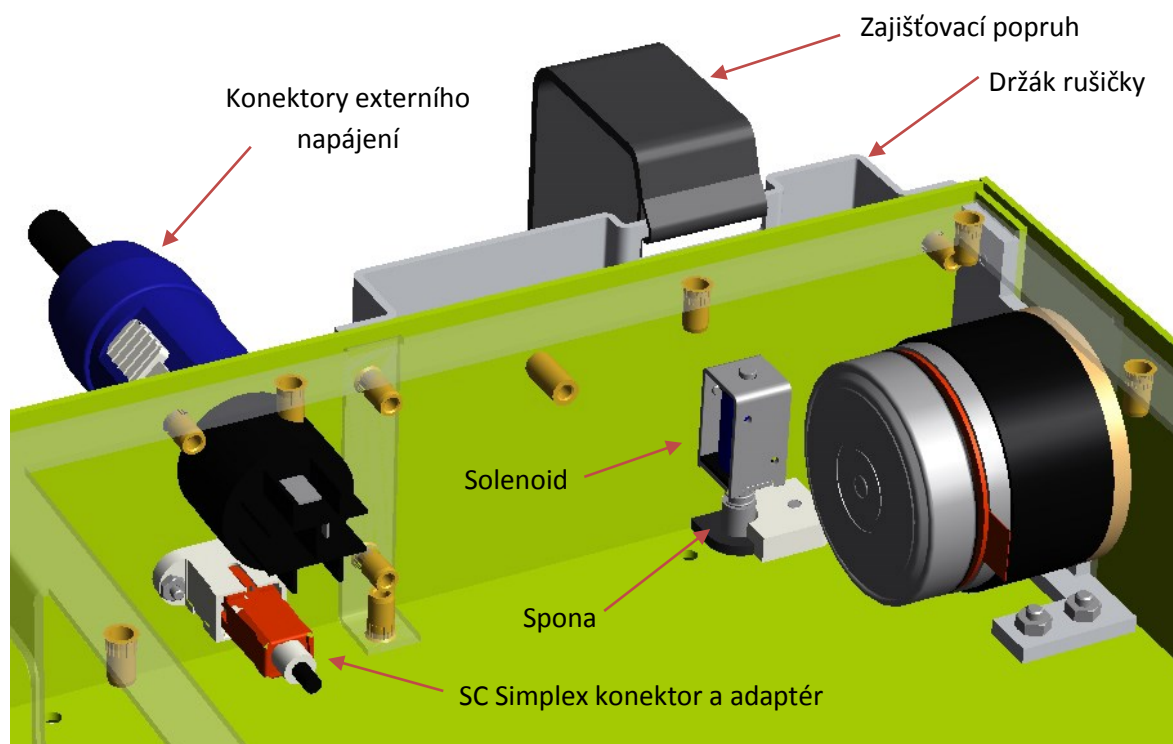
Robot – 3. Stádium – Nosný rám
